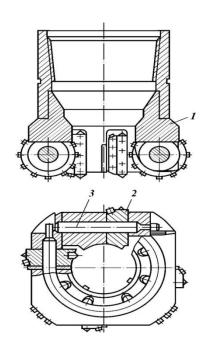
Схема устройства бурильной головки режуще-дробящего действия типа СЗ: 1- муфта с присоединительной резьбой; 2- корпус; 3- шарошка
